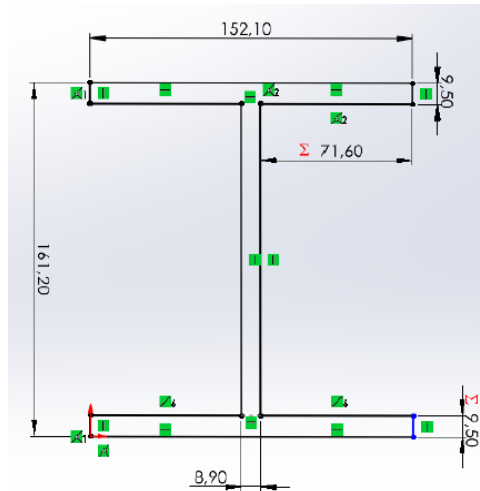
Géométrie typique d'une extrusion en I 6005A-T6
